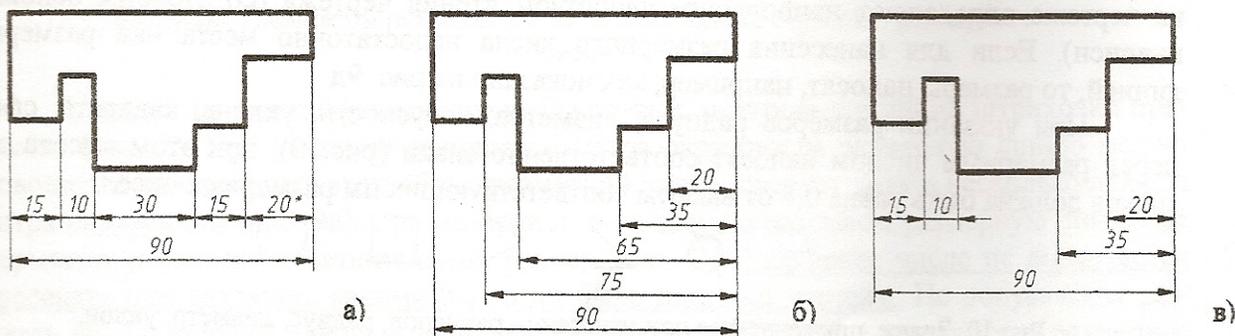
Способы нанесения размеров: а – цепочкой; б – от базы; в – комбинированный
